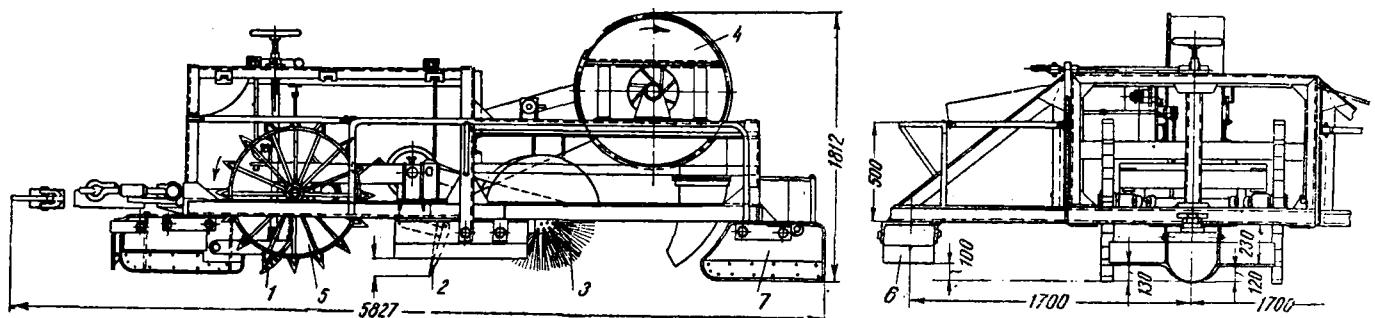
Агрегат Э. Я. Витковского для ухода за ледяными одноколейными дорогами (изготовленный Ликинским заводом)
